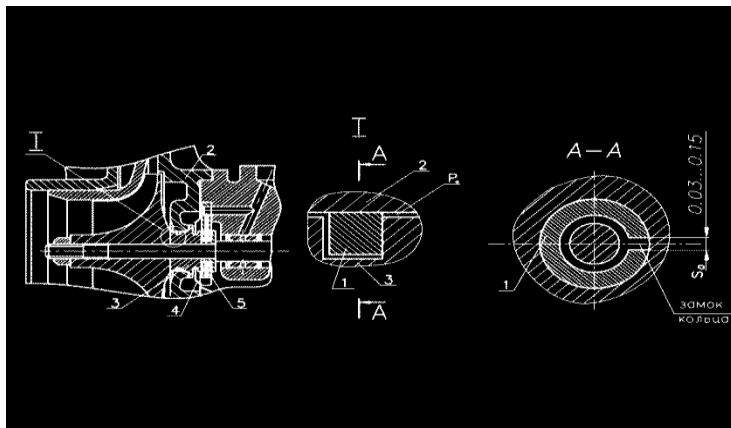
Уплотнение упругим металлическим кольцом компрессорной ступени у турбокомпрессоров ТКР 7С: 1 – уплотнительное кольцо; 2 – крышка; 3 – маслоотражатель; 4 – маслосбрасывающий экран; 5 – упорный подшипник
